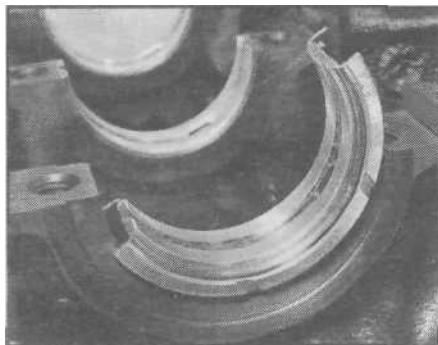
,а. Установка вкладыша среднего подшипника с фланцами в постель блока цилиндров
